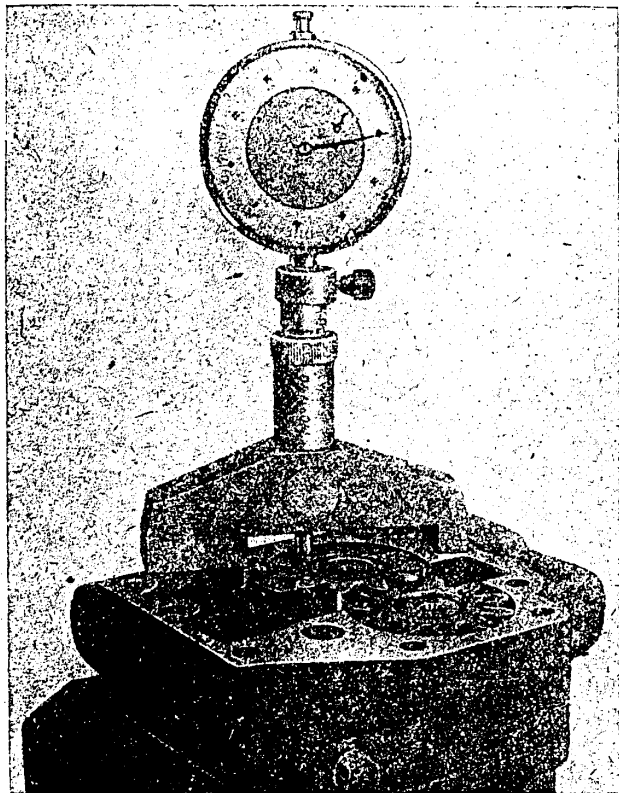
Rückstehmaß der Ölpumpenräder ausmessen (Werkzeug Nr. 324.020-M 133)
